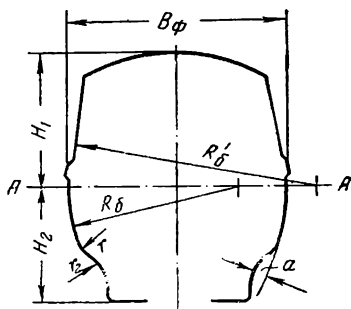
Основные размеры профиля боковины покрышки по прессформе:
